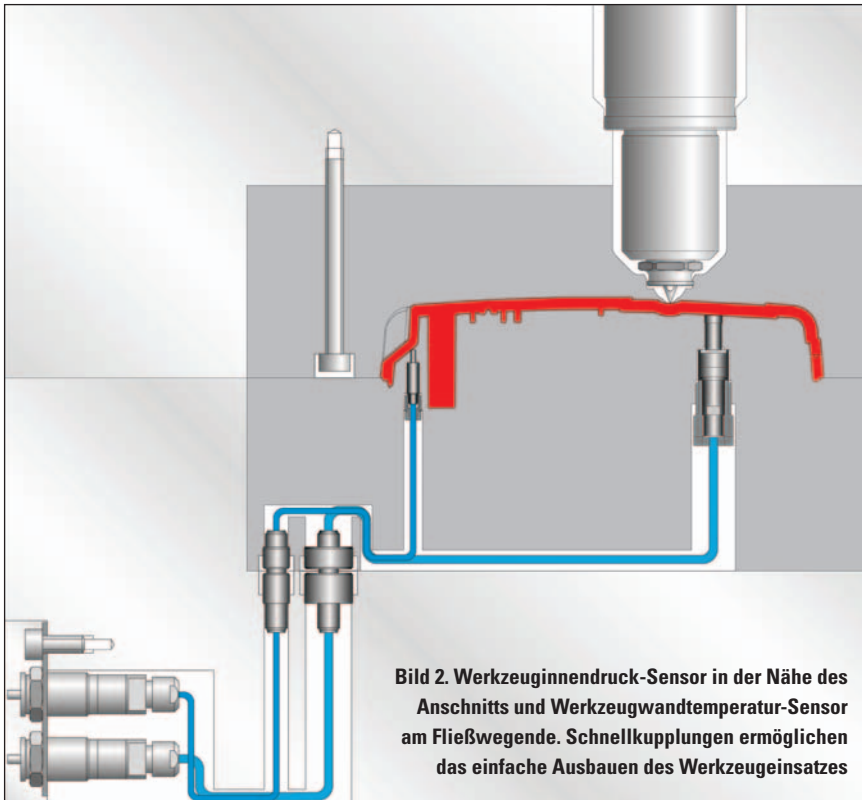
Werkzeuginnendruck-Sensor in der Nähe des Anschnitts und Werkzeugwandtemperatur-Sensor am Fließwegende. Schnellkupplungen ermöglichen das einfache Ausbauen des Werkzeugeinsatzes
